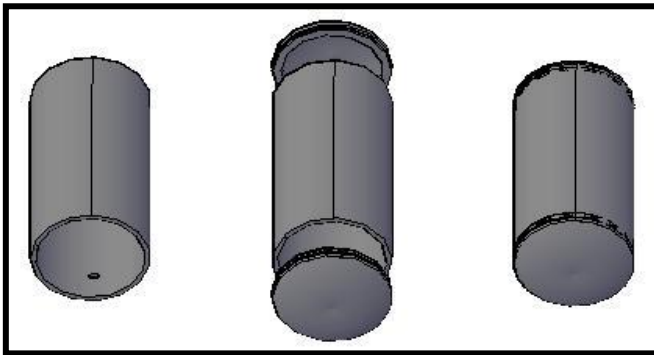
Esquema tridimensional da soldagem dos tampos ao corpo cilíndrico do reservatório.
